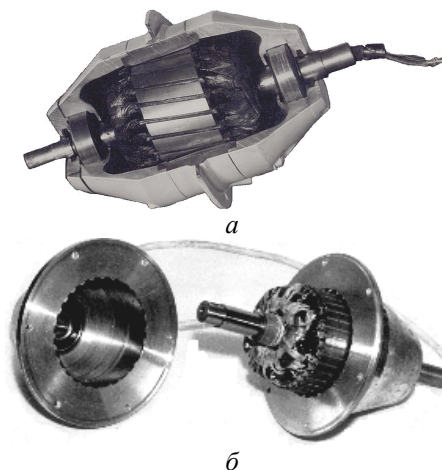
Варианты обращенного двигателя: а – с установкой ротора в двух подшипниковых щитах; б – с двухсекционным конусно-плоскостным магнитопроводом и отлитыми заодно с обмоткой корпусами установки подшипников
